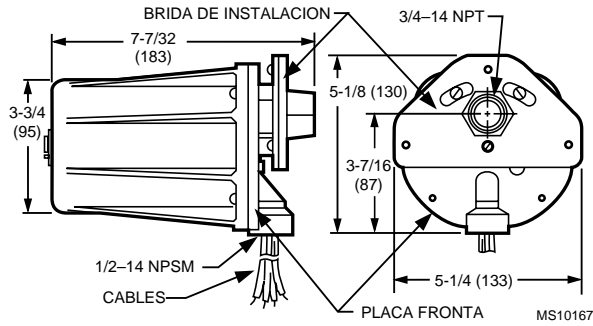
Dimensiones del C7061A en pulg. (mm)
